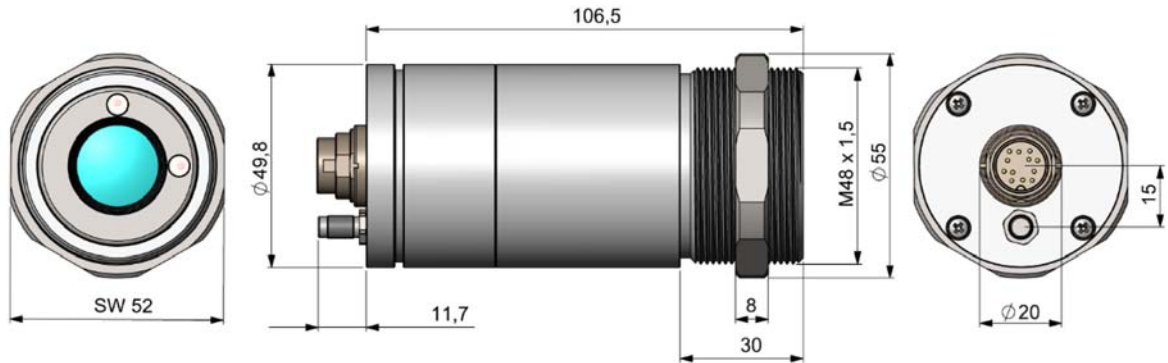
Maßzeichnung thermoMETER CTVideo-Sensor (Standardversion)
